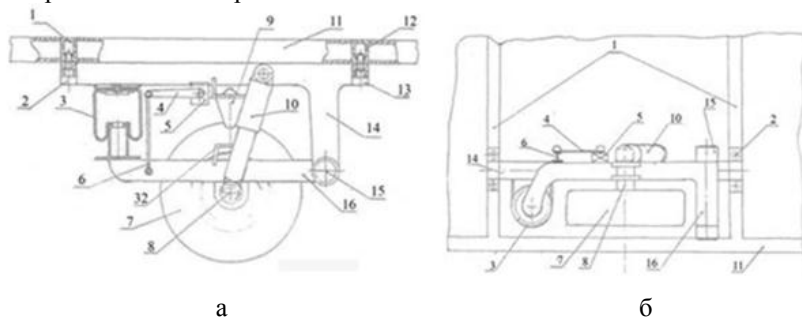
Схема розташування деталей та вузлів лівої підвіски причепа в транспортному положенні, а - вигляд спереду, б-вигляд знизу
